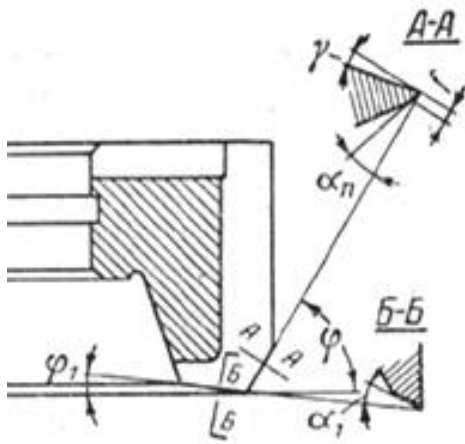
Геометрические параметры зуба торцовой фрезы [6]
